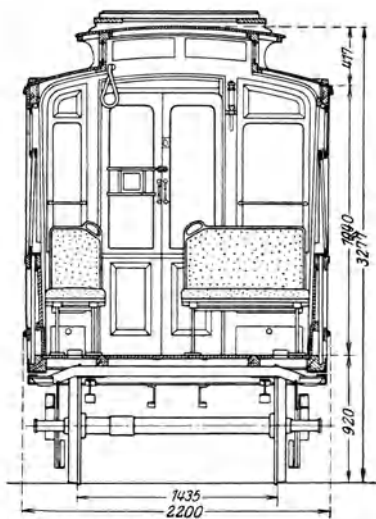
Querschnitt durch einen Triebwagen mit besonderem Untergestell und Laternendach.
